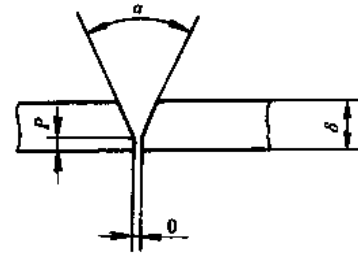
单面焊双面成形三丝埋弧焊
